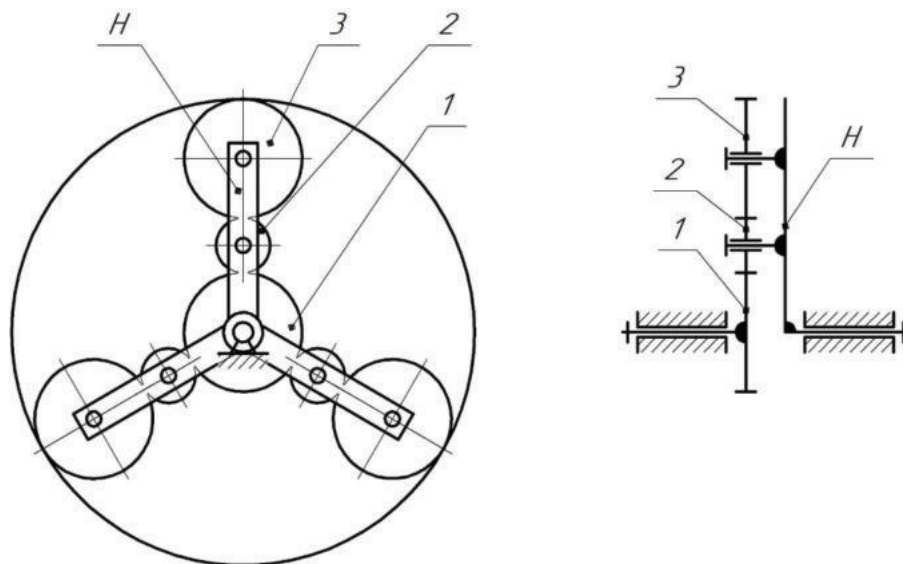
Кинематическая схема зубчатого механизма привода гусеницы
